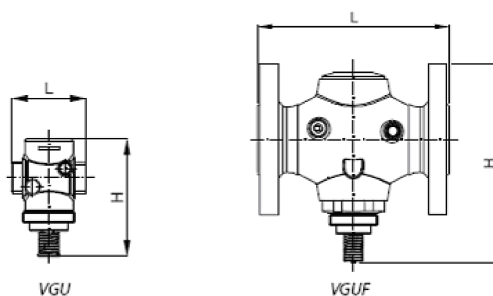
Габаритные и присоединительные размеры клапанов VGU, VGUF
